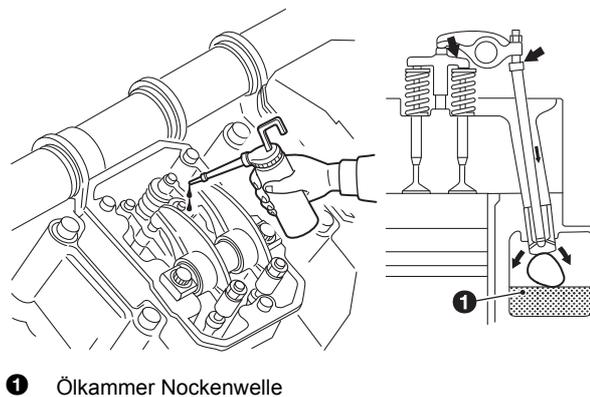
Motoröl auf Ventilmechanik und Kammer spritzen
